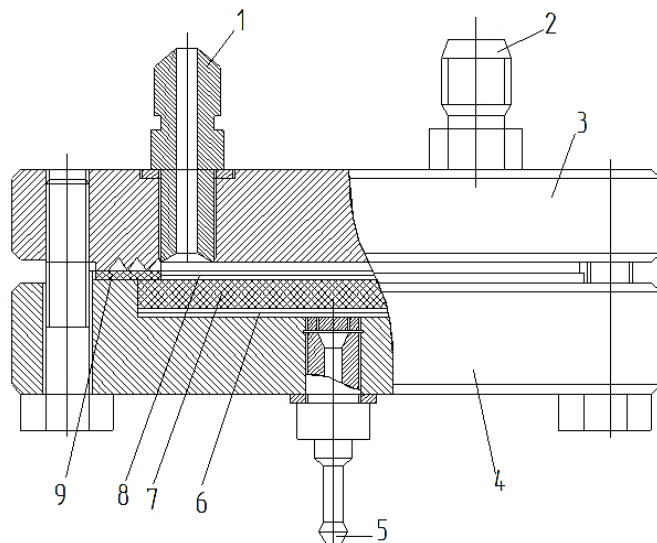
Схема ячейки для испытания мембран: 1 – штуцер для подачи исходного раствора; 2 – штуцер для отвода концентрата; 3 – верхняя крышка ячейки; 4 – корпус ячейки; 5 – штуцер для отвода пермеата; 6 – мембрана; 7 – пористая подложка; 8 – дренажная сетка; 9 – прокладка
